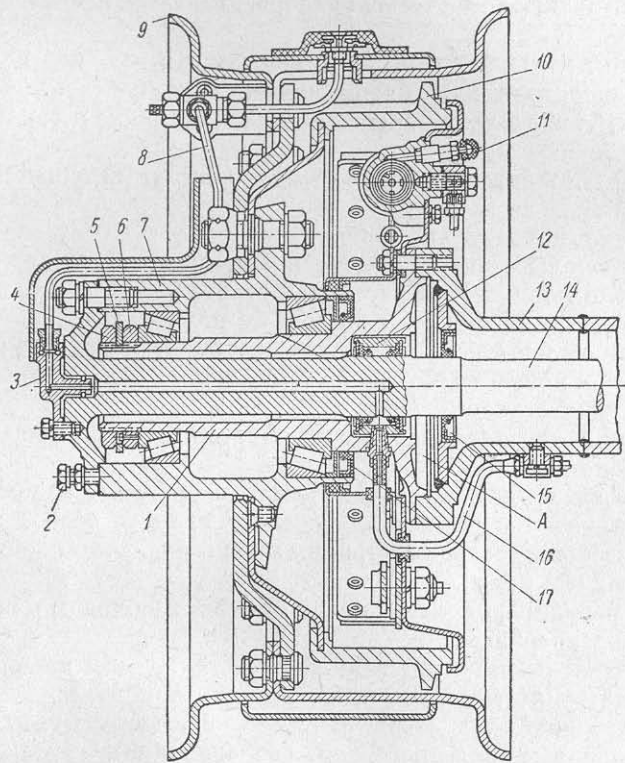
Ступица заднего колеса автомобиля с системой регулирования давления в шинах:
